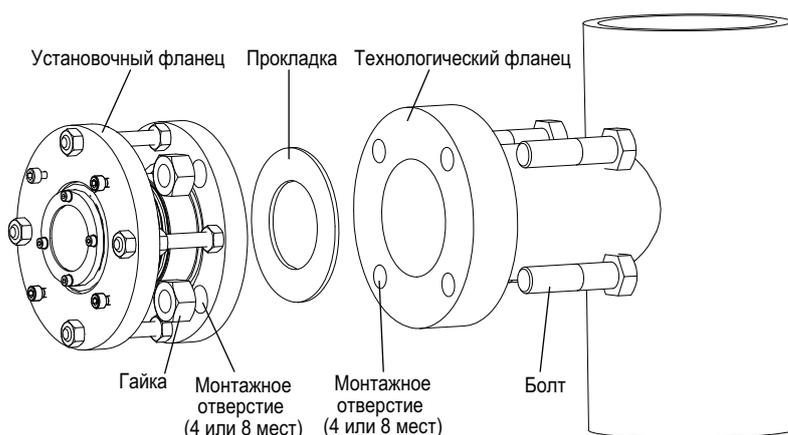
Установка выравнивающего (установочного) фланца
